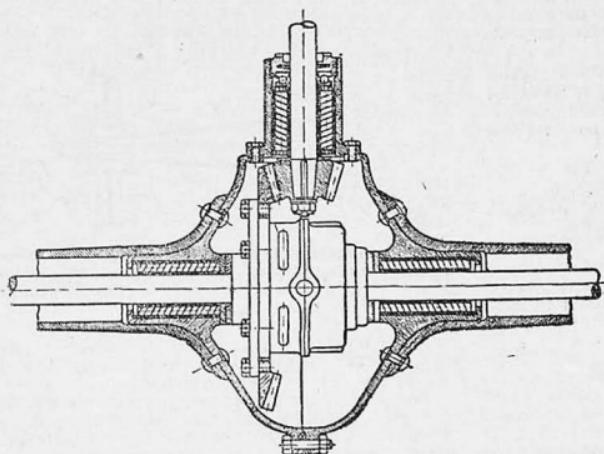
Установка подшипников ведомой шестерни непосредственно на полусях
